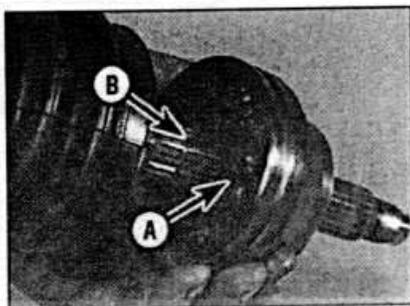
При установке приводного вала в наружный шарнир стопорное кольцо (А) должно установиться в канавки приводного вала (В).
